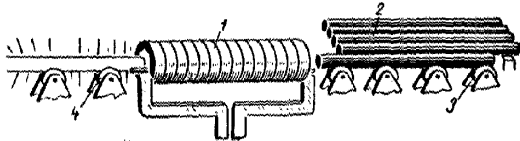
Схема методического нагревателя с непрерывным движением заготовок:
